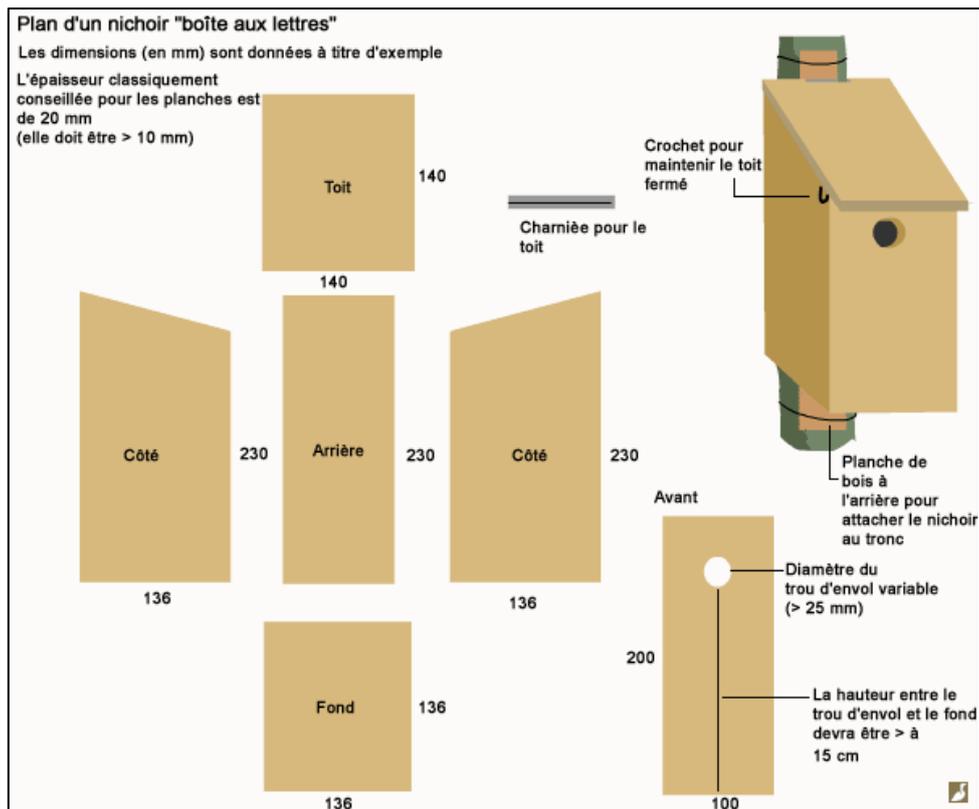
Plan de fabrication d'un nichoir type « boîte aux lettres » permettant d'accueillir des petits passereaux (source : [jardiner-autrement.fr](http://jardiner-autrement.fr)).
